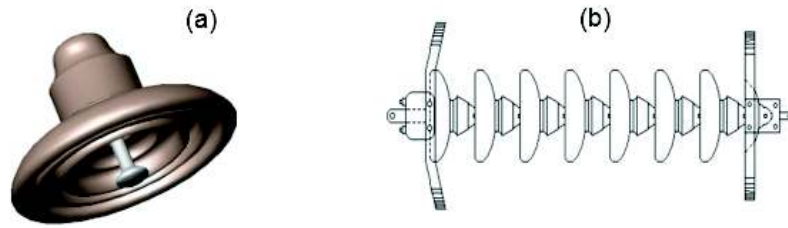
a) Aislador de Suspensión, b) Cadena de Aisladores
